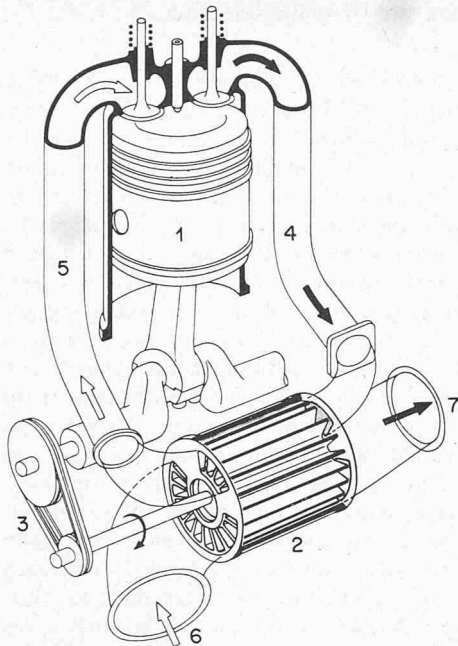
Druckwellenmaschine Compress als Aufladeaggregat. 1 Motor, 2 Zellenrad, 3 Riemenantrieb, 4 Hochdruck-Abgas, 5 Hochdruck-Luft, 6 Niederdruck-Lufteinlass, 7 Niederdruck-Gasauslass
